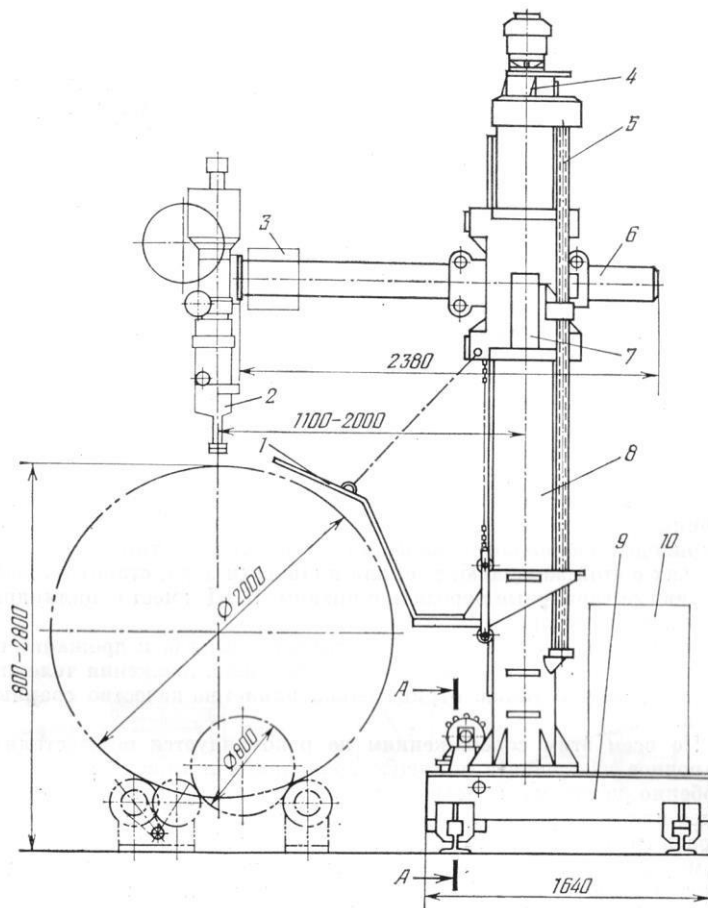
Глагольная тележка ГТ-1: 1 – щиток-подлокотник; 2 – сварочная головка; 3 – пульт управления; 4 – механизм подъема каретки; 5 – подъемный винт; 6 – выдвижная штанга; 7 – каретка; 8 – колонна; 9 – тележка; 10 – шкаф аппаратуры управления
